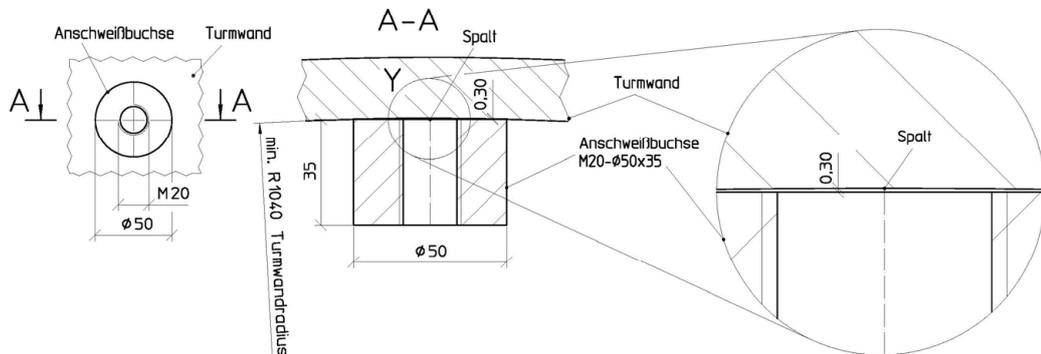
Detail Anschweißbuchse auf gekrümmten Mantelblechen
